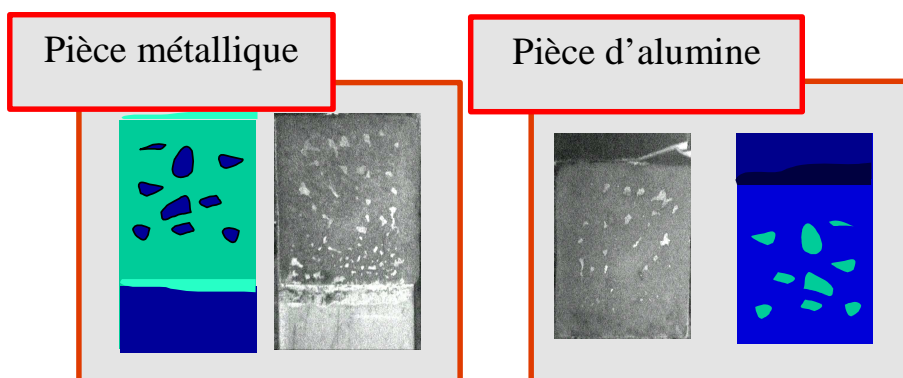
Photographies et schémas des interfaces des pièces cisailées
